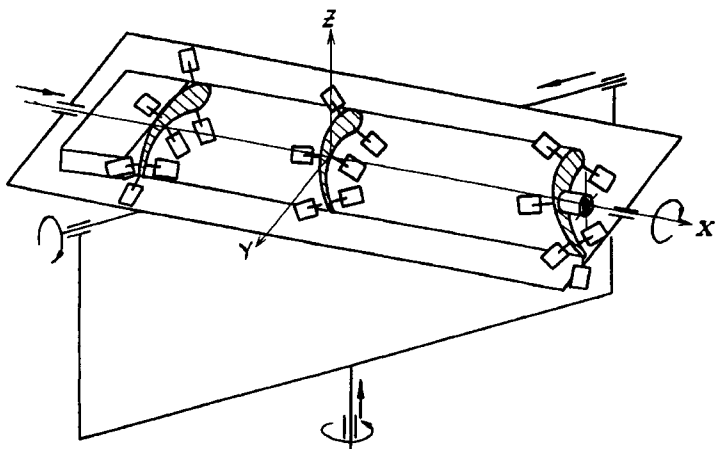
Автоматическая установка заготовки лопатки турбины, обеспечивающая равномерное распределение припуска на лопасти
